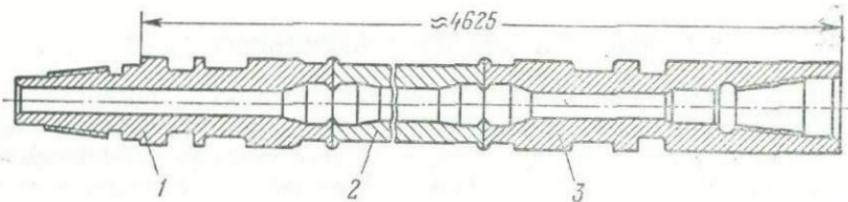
Утяжеленная бурильная труба с приваренными соединительными концами:
